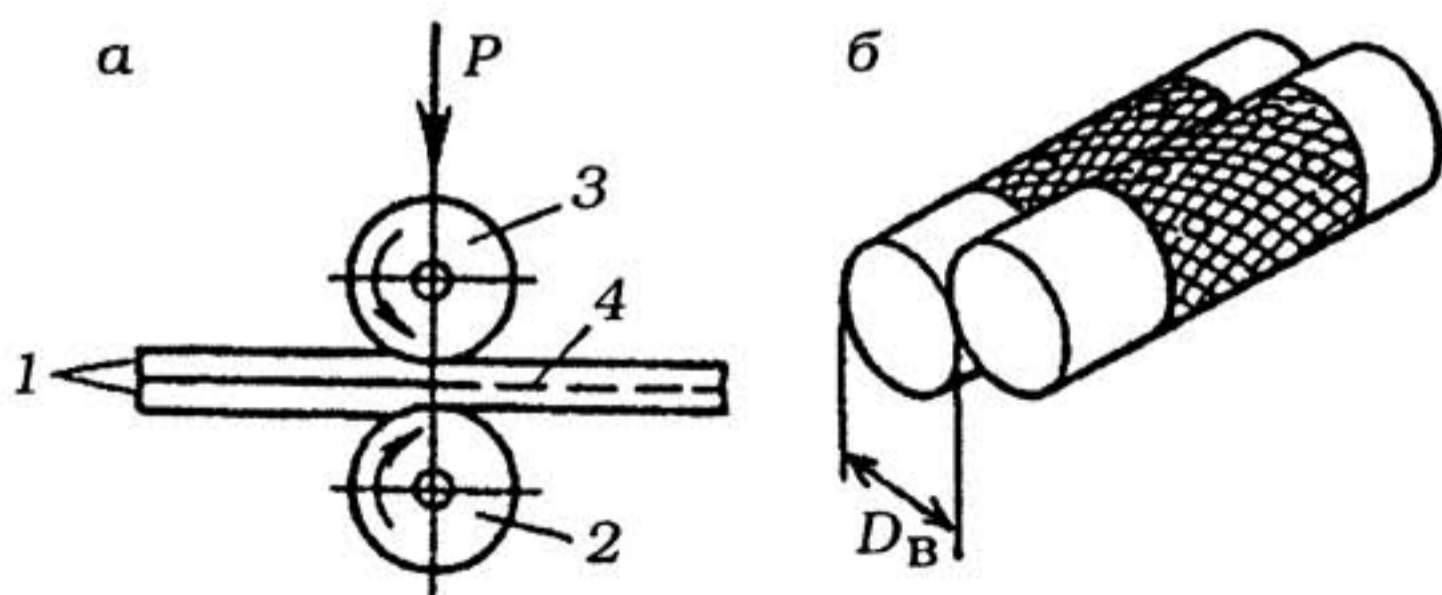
Схемы роликковой контактно-тепловой сварки (а) и валков (б): 1 — свариваемый материал; 2 — нагретый ролик; 3 — прижимный ролик; 4 — сварной шов
